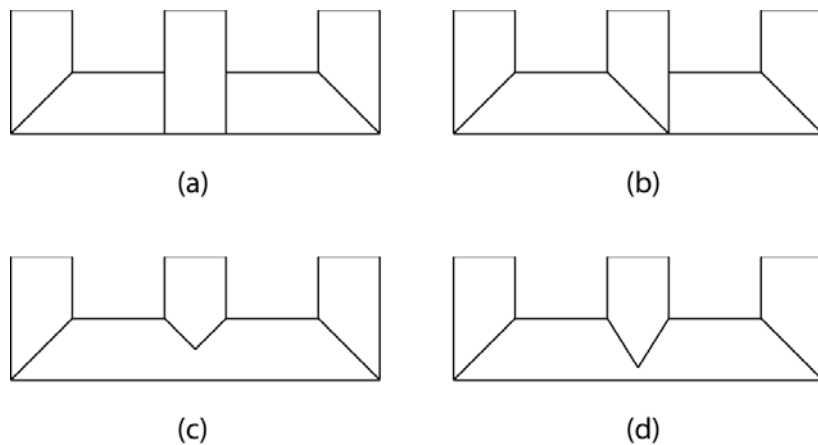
Géométrie du T joint : (a) le joint à 90° , (b) le joint à $45^\circ-90^\circ$, (c) le joint à 45° et (d) le joint à 60° .
